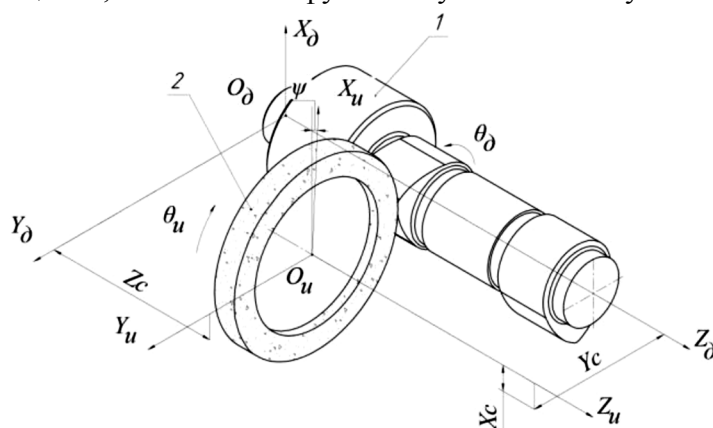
Розрахункова схема шліфування розподільного вала:
